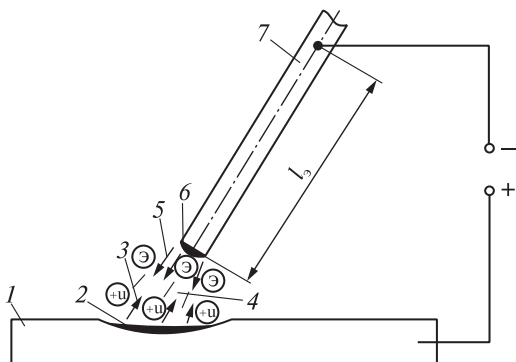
Схема сварочной дуги постоянного тока
